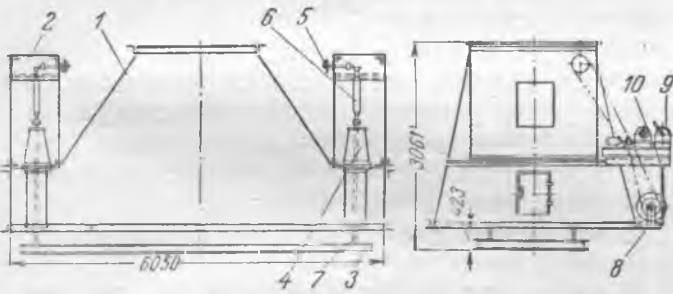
Блок верхней части корпуса электрофильтра ДВП-4-20 вместе с приводом и изоляторными коробками.
